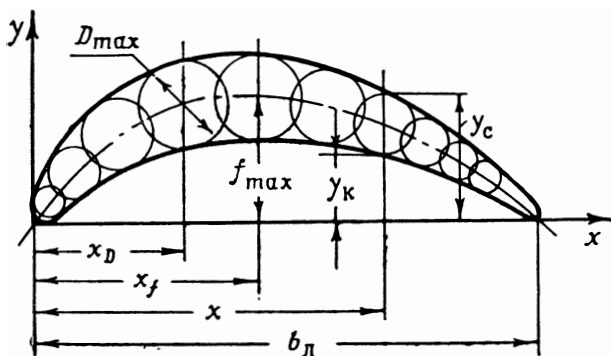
Лопаточный профиль с обозначением основных размеров
